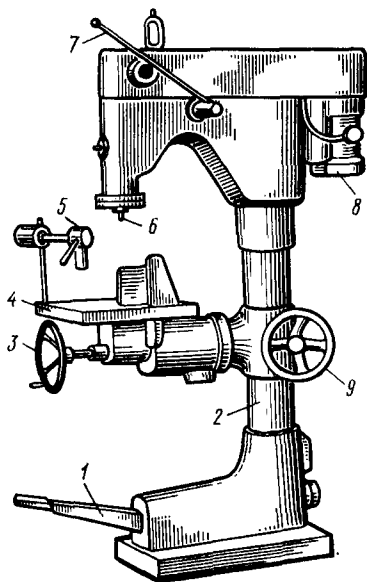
Сверлильный одношпиндельный станок СВА-2М:
